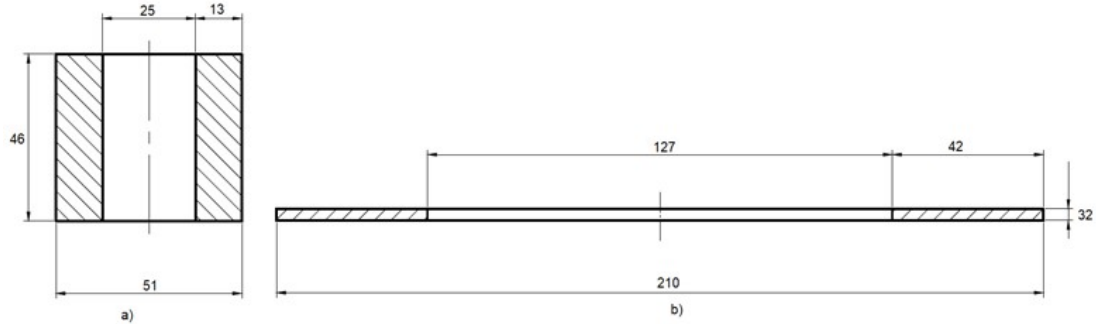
Pieza de trabajo: a) Dimensiones iniciales; y b) dimensiones finales.
